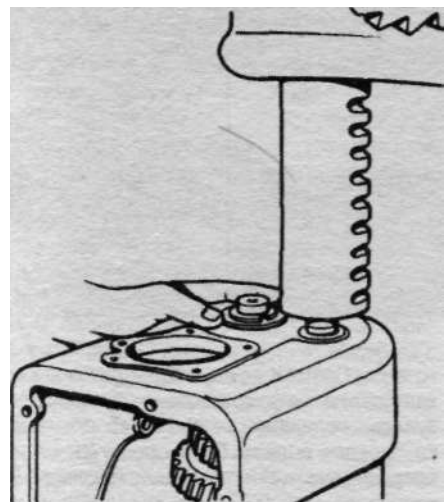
Запрессовка оси блока шестерен заднего хода
